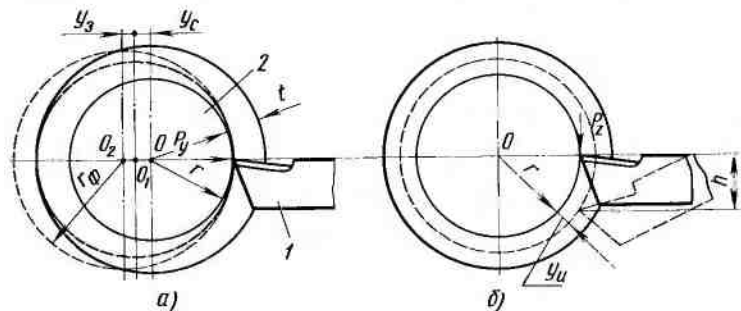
Схема упругих перемещений при токарной обработке: а — смещение оси заготовки из-за отжатий станка и заготовки, б — смещение вершины резца от центра заготовки из-за его отжатия и прогиба
